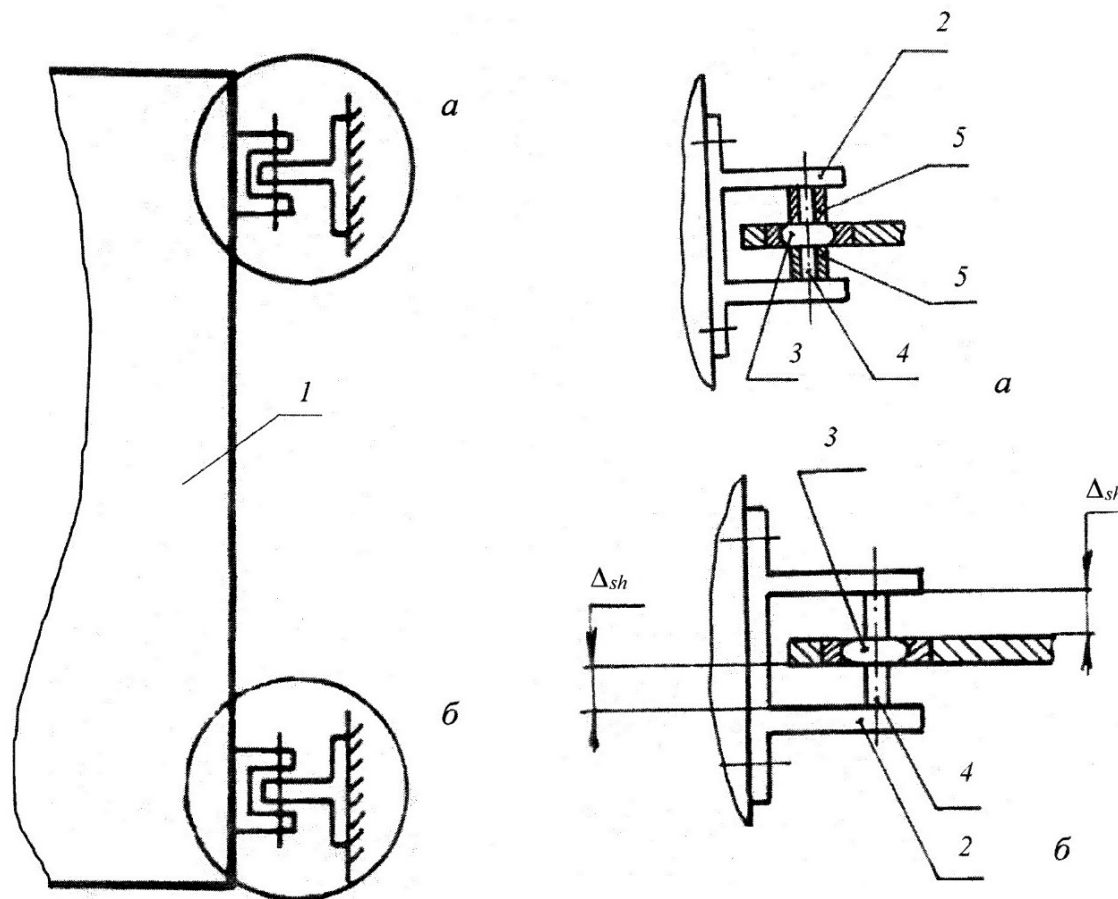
Шарнирный узел штанги, образованный двумя сферическими шарнирами с шарнирными подшипниками (например, по ГОСТ 3635–78): *a* – шарнир без тепловой развязки; *б* – шарнир с тепловой развязкой; 1 – корневая часть штанги; 2 – проушина шарнира; 3 – вилка шарнира с подшипником; 4 – ось шарнира; 5 – распорные втулки
